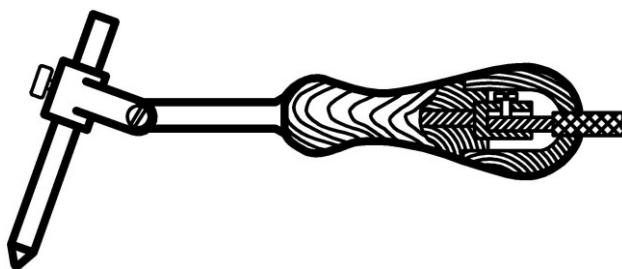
Тримач М. М. Бенардоса для ручного дугового зварювання
